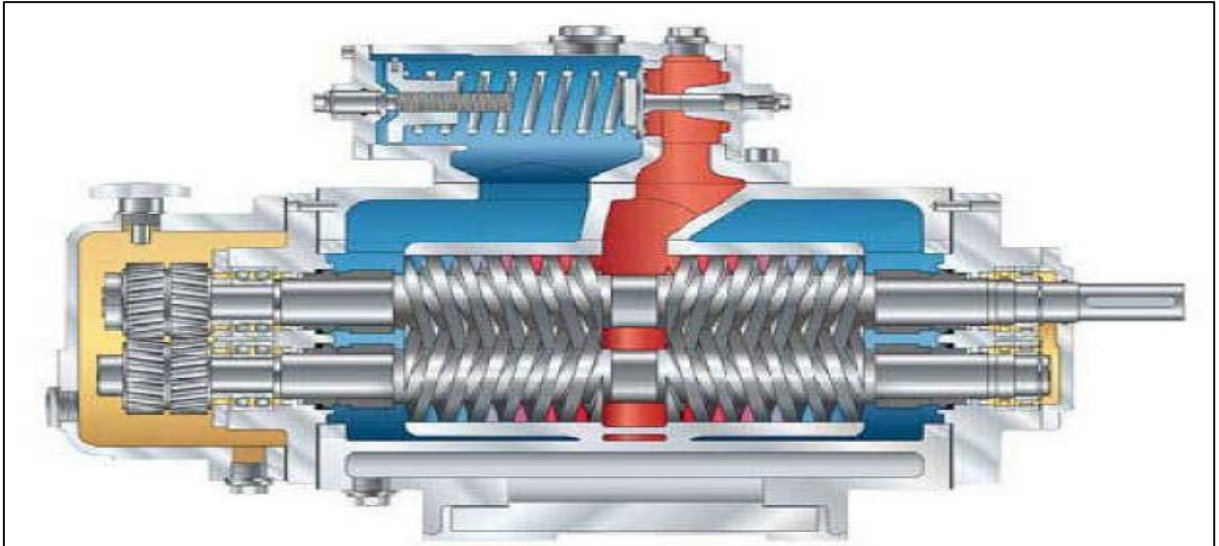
Dessin en coupe d'une pompe multiphasique à double vis. [2]
